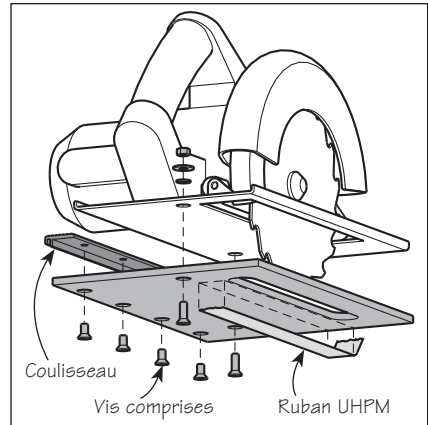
Montage d'une scie circulaire et du coulisseau sur la semelle auxiliaire
